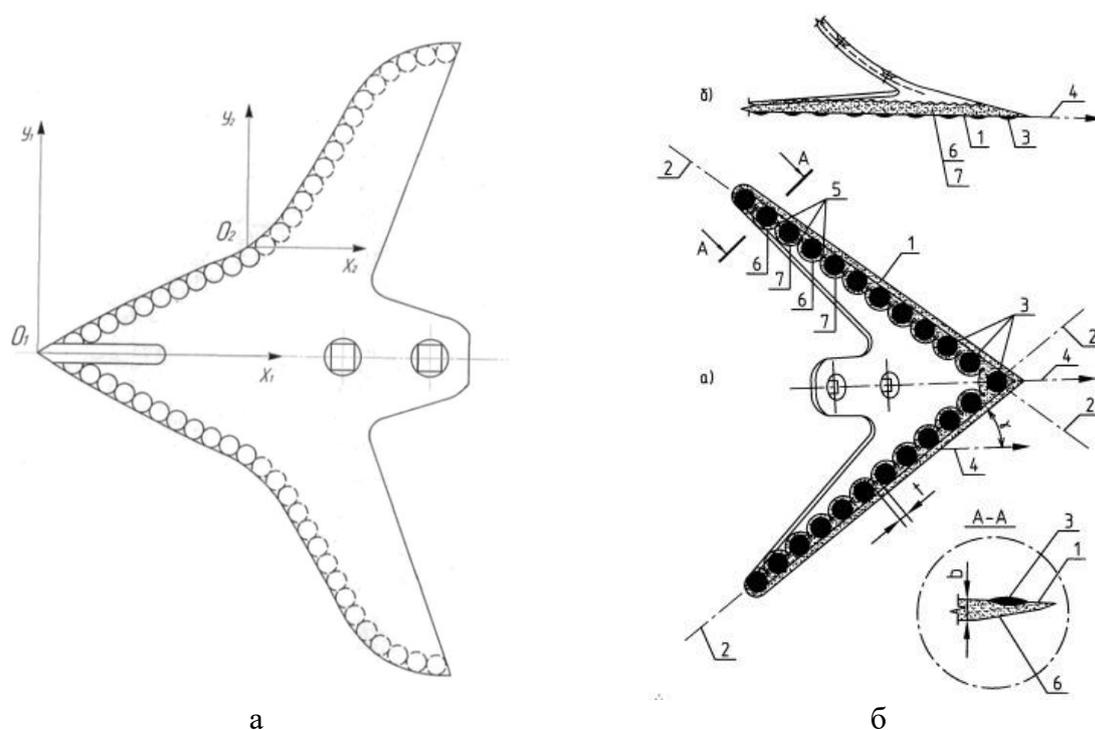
Упрочнение лап культиватора наплавкой зон в виде кругов: а – схема наплавки согласно [83, 84]; б - [85]: 1 - культиваторная лапа, 2 - линии армирования, 3 - точки износостойкого материала, 4 - направление перемещения рабочей поверхности, 5 – перекрытие зон термического влияния, 6 и 7 – соседние точки
